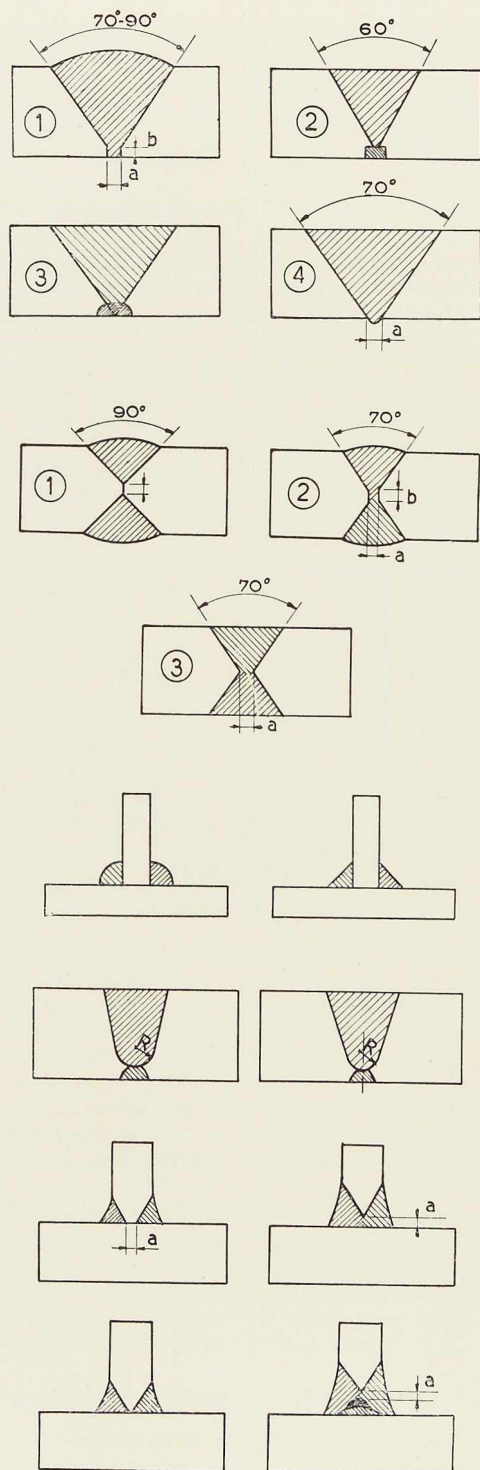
Exemples montrant quelques bonnes et mauvaises exécutions de détails de soudure.
